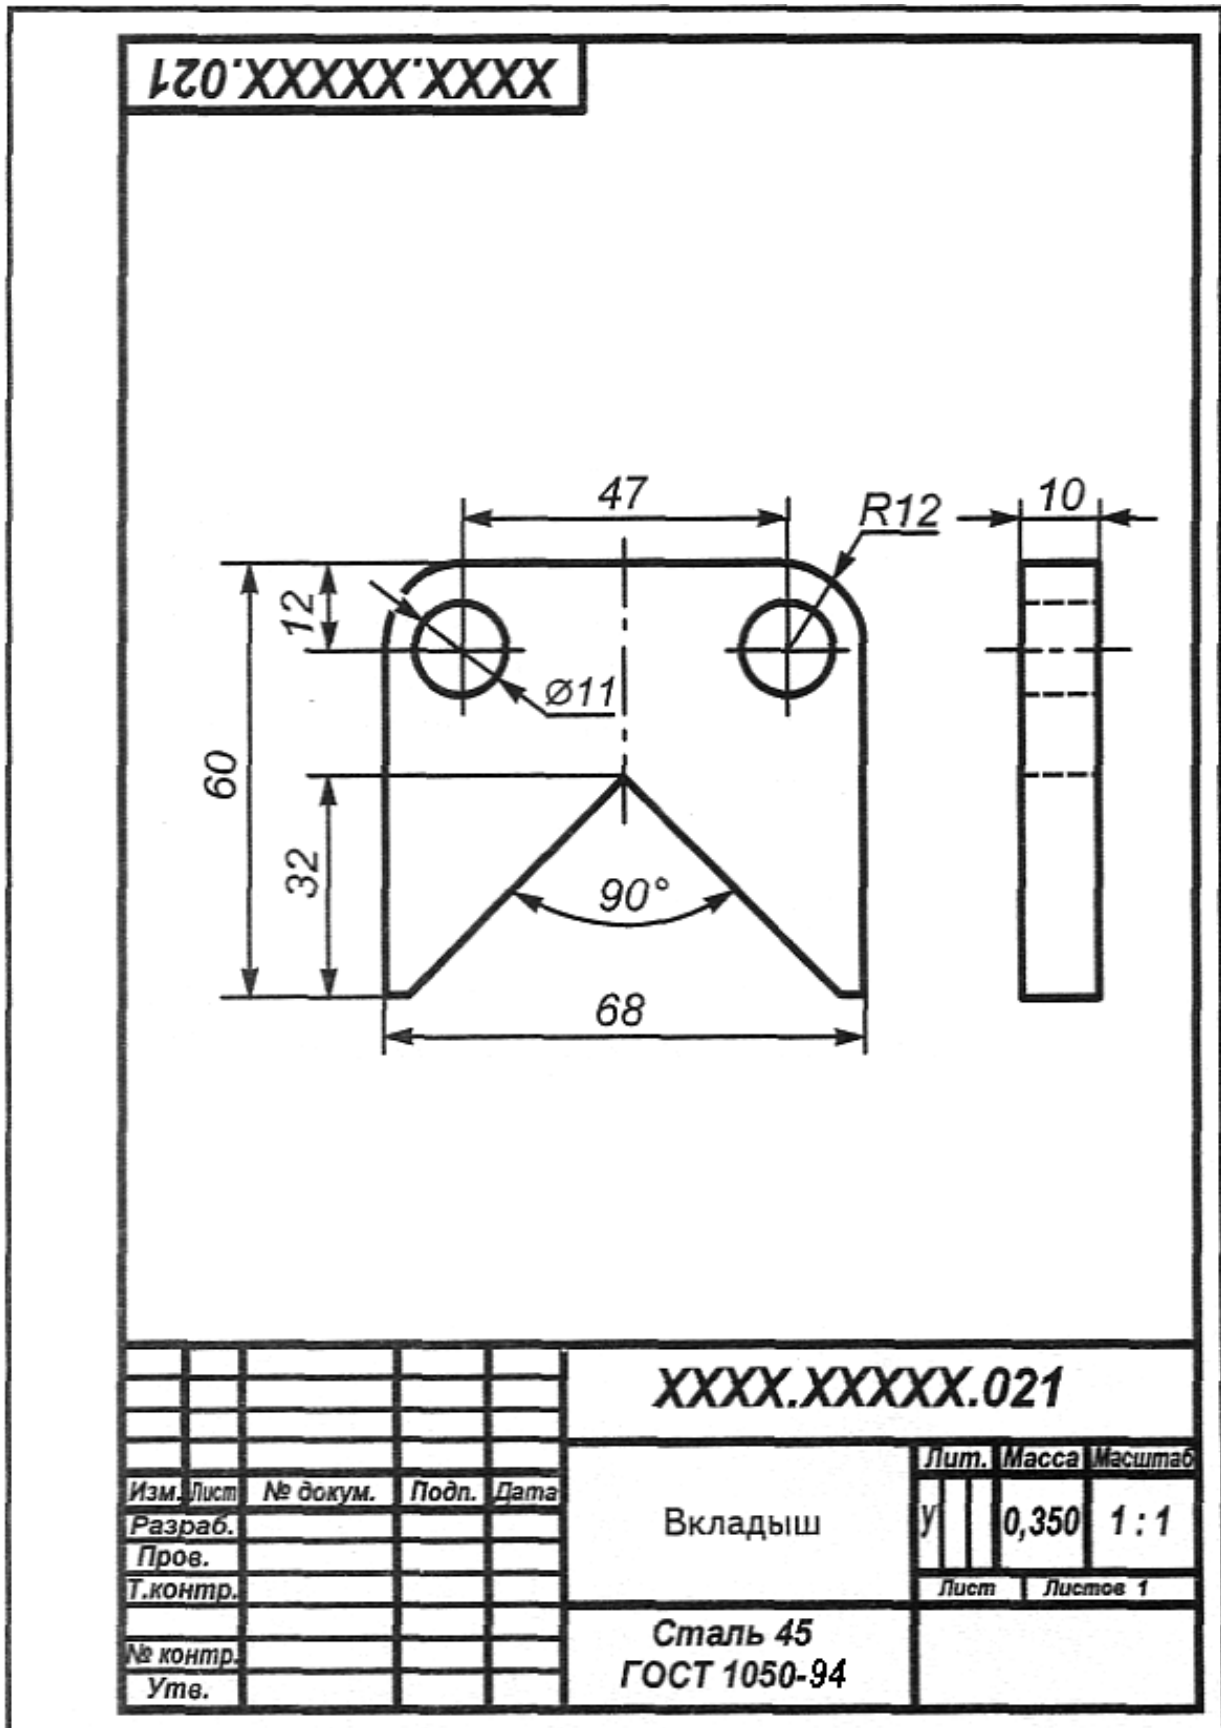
Рабочий чертеж детали «Вкладыш»
